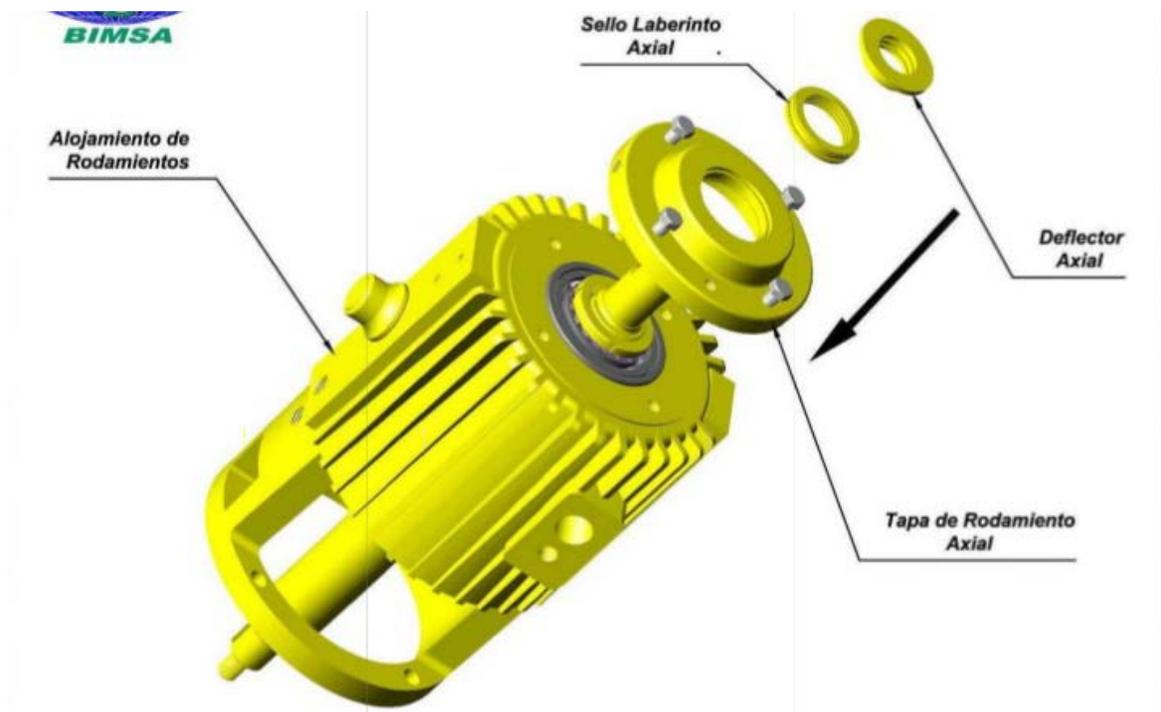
ENSAMBLE DE TAPA AXIAL
